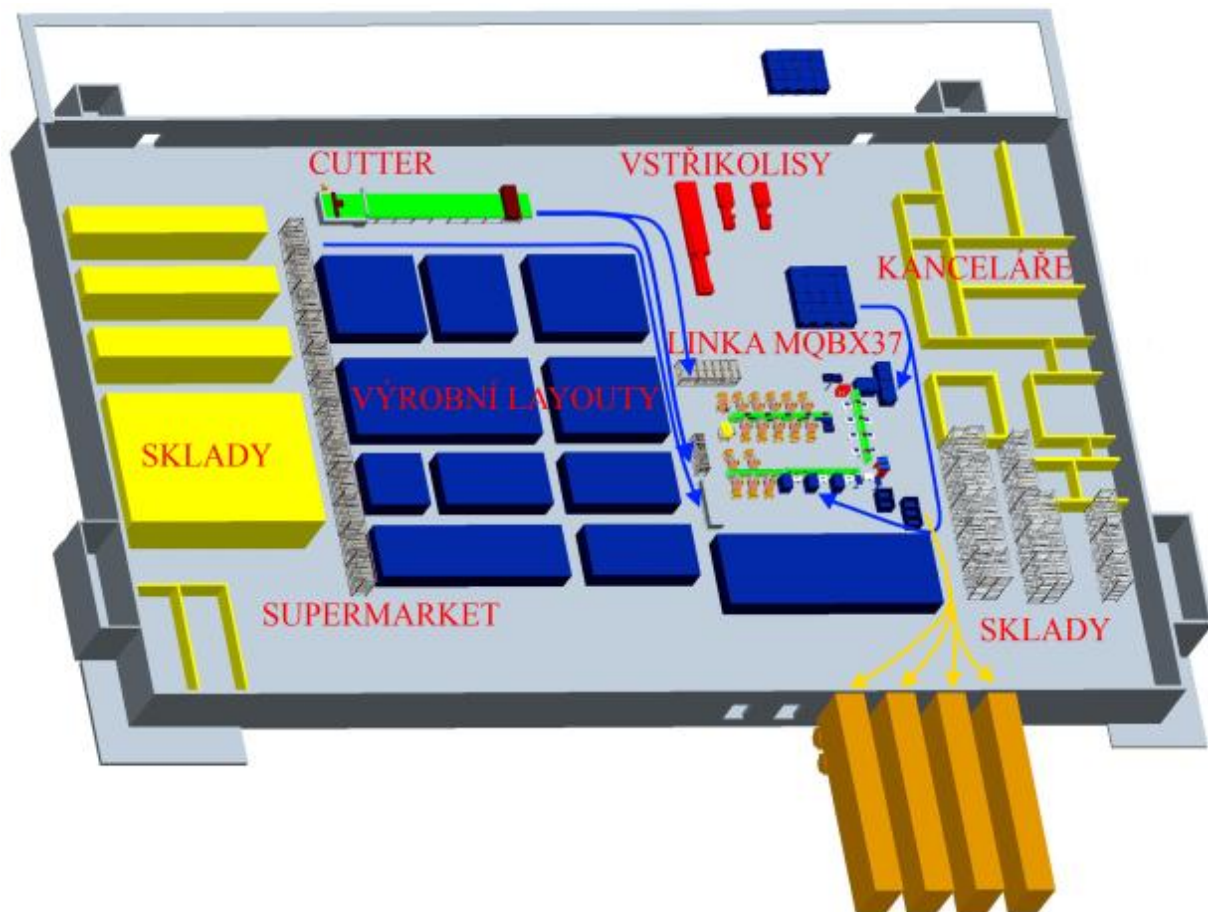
3D layout výrobní linky MQBx37 varianta B
